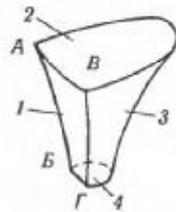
Поверхні підбора: 1 — фронтальна (АВ, ВГ — крокулі підбора); 2 — верхня площадка; 3 — бічна; 4 — нижня
